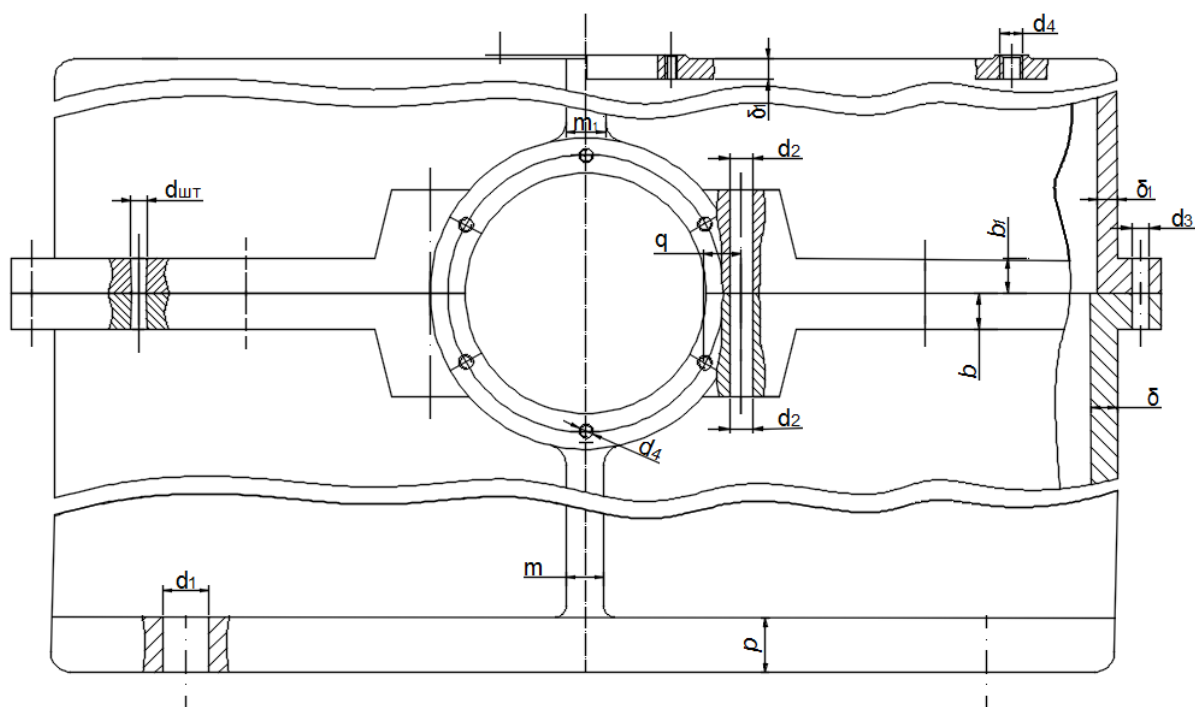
Конструктивные размеры корпуса редуктора
